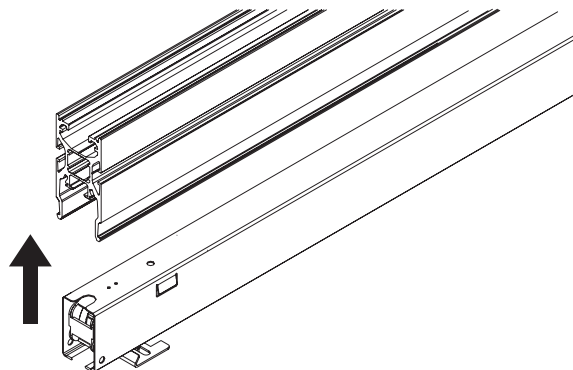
Enganche de la canaleta para cables en el carril Multi-Lane
